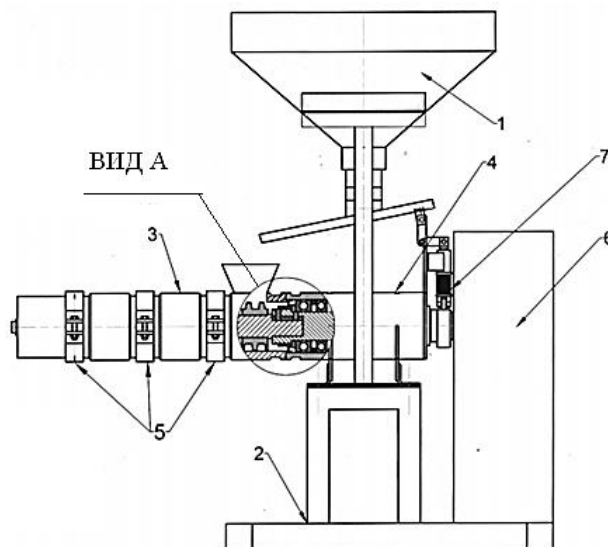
Общий вид устройства для экструдирования зернового корма: 1 - бункер; 2 - станина; 3 - рабочая часть; 4 - шпиндель; 5 - хомут крепления; 6 - защита привода; 7 - механизм подачи смеси
